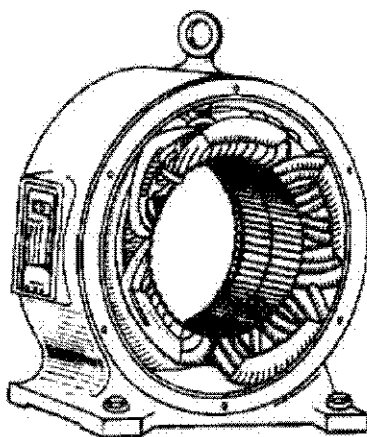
Внешний вид статора со стороны лобовой части трехфазной обмотки
